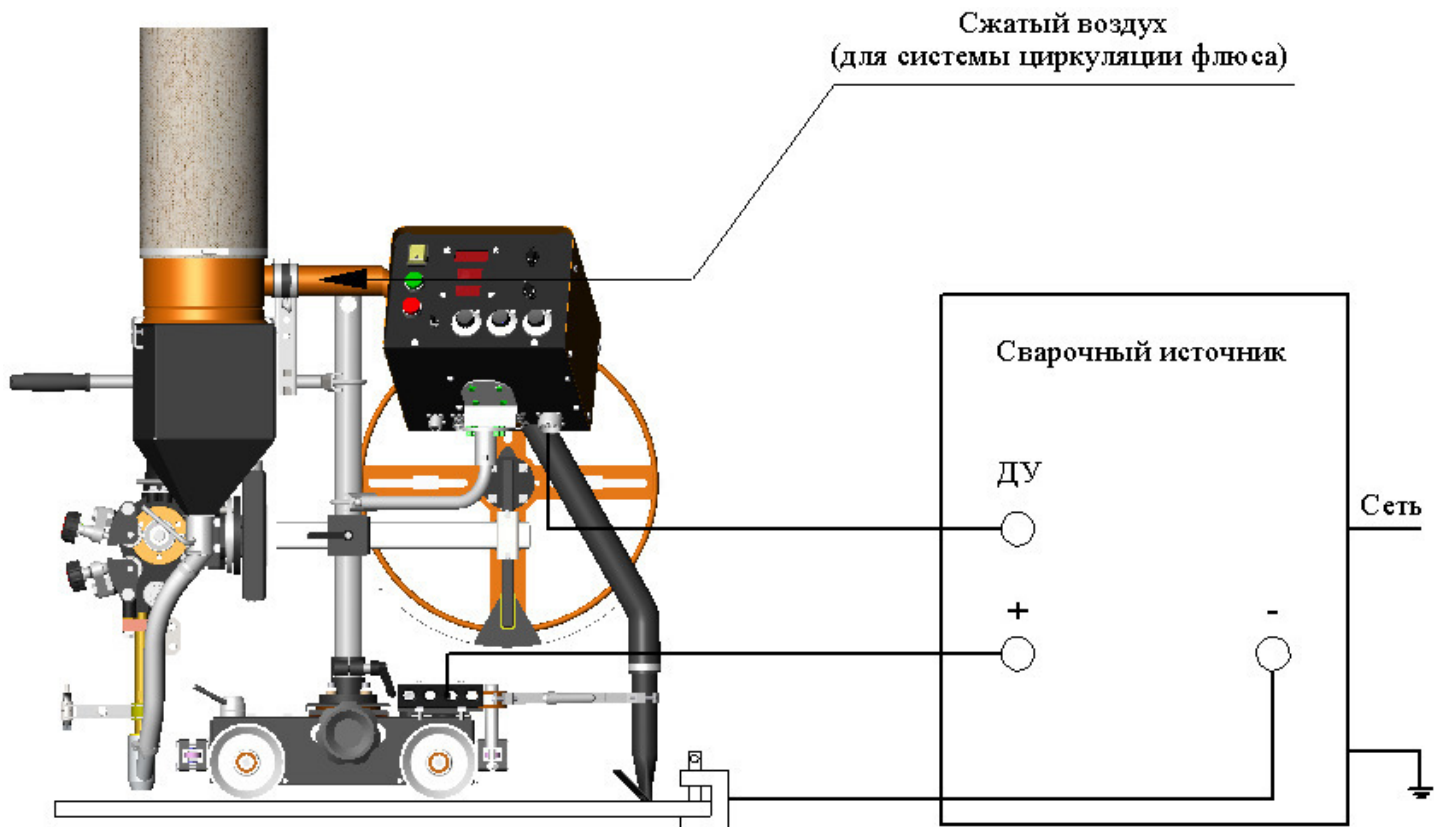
Схема подключения автомата для сварки SAW и TWIN.
